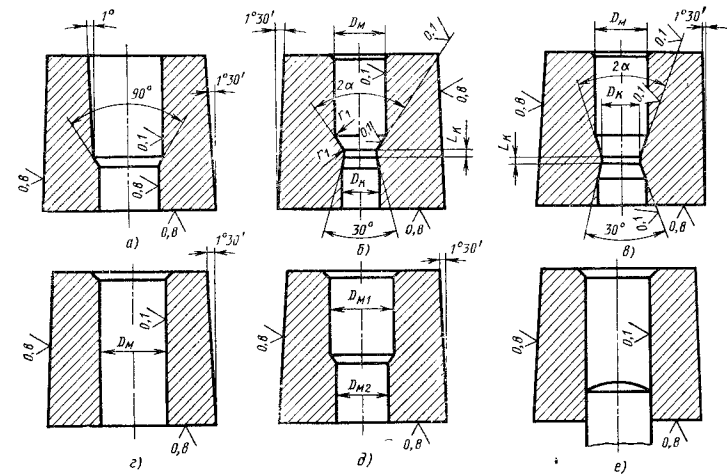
Конструкции матриц для холодной объемной штамповки:
